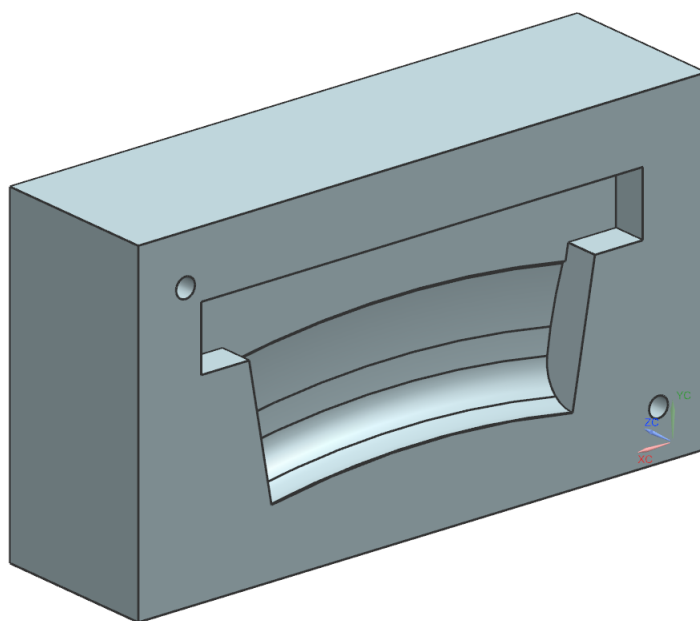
Molde Exterior. Diseño del molde exterior. (Fuente: Propia)
